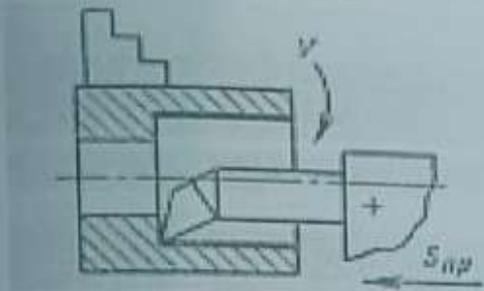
Схема обработки заготовок на токарно-винторезном станке, упорно-расточной резеи.
